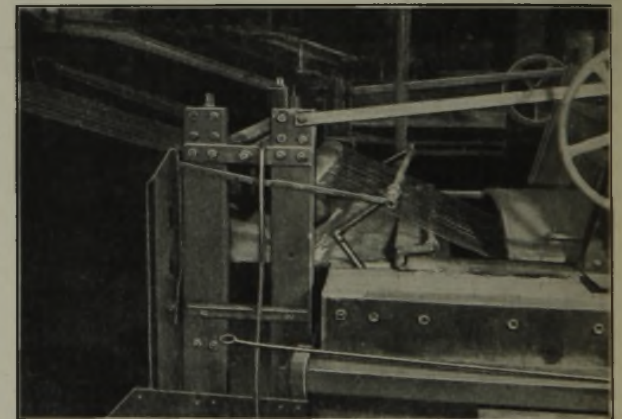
Drahtaustritt nach dem Durchgang durch das Salzbad.
